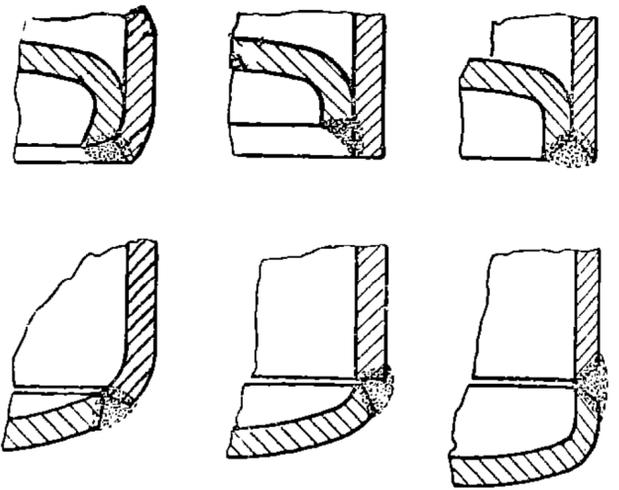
Schweißung bei Hohlkörpern mit Druckbeanspruchung.
